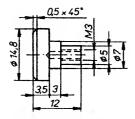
Kotúč I kľbu. Materiál: gulatina Fe. Úprava: zinkovanie. Dva kusy
